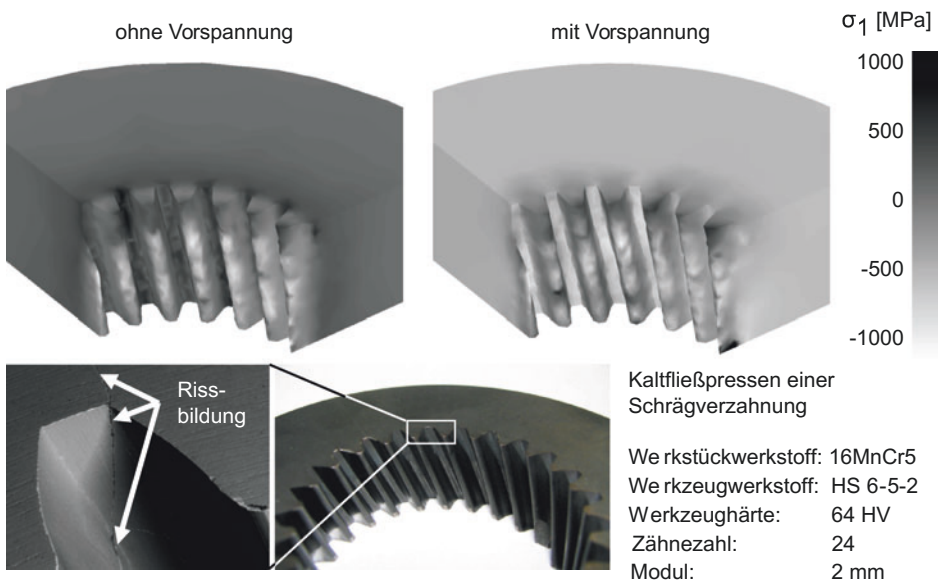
3D-Simulation der Belastungen einer Werkzeugmatrize zum Querfließpressen einer Schrägverzahnung
